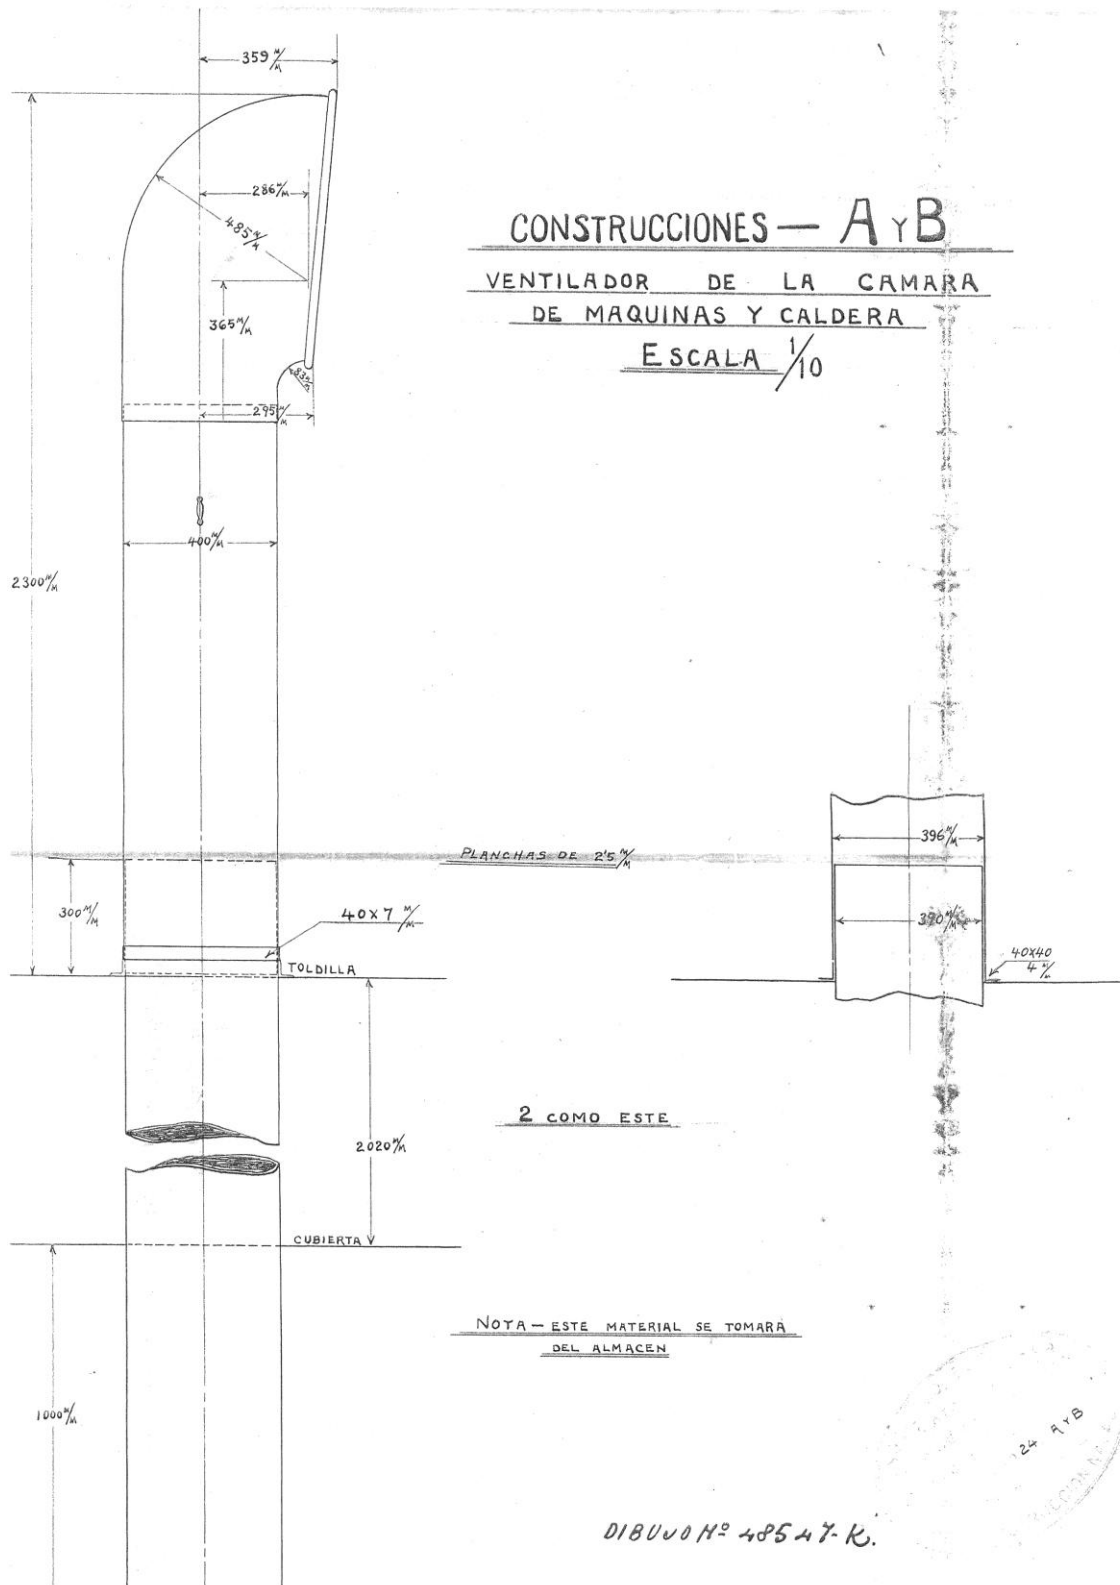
Ventilador de la cámara de máquinas y caldera.
